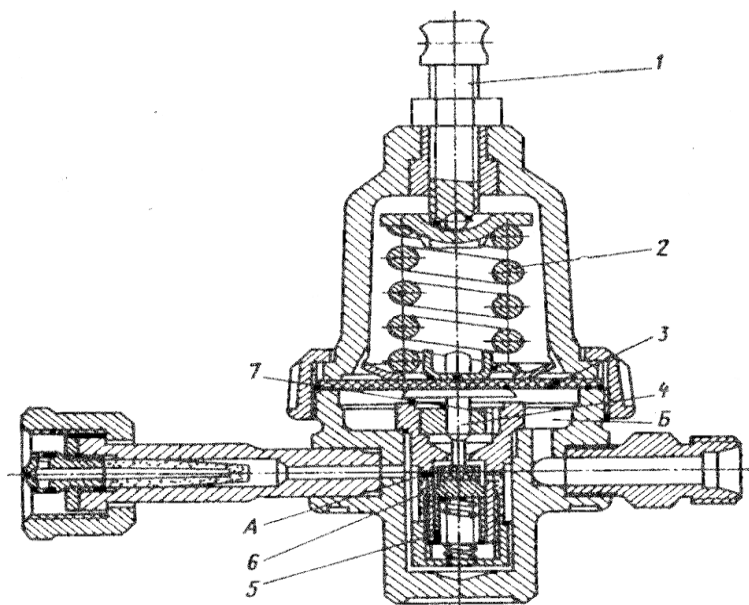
Схема одноступінчатого редуктора високого тиску
